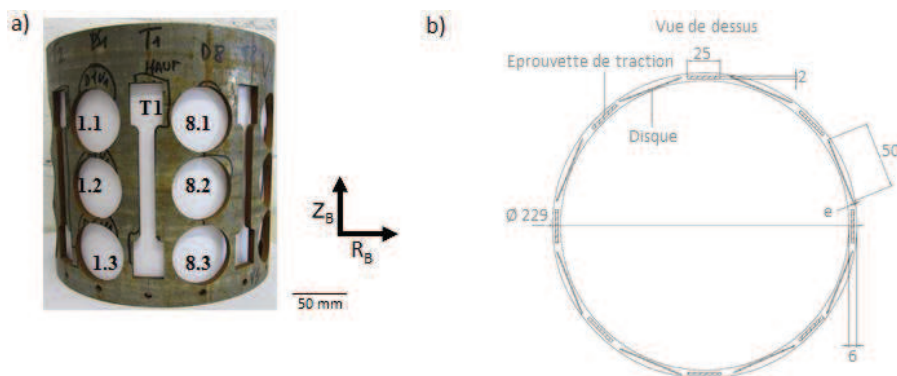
Plan de découpe des échantillons : a) un disque et b) une éprouvette de traction. Les dimensions sont en mm.
